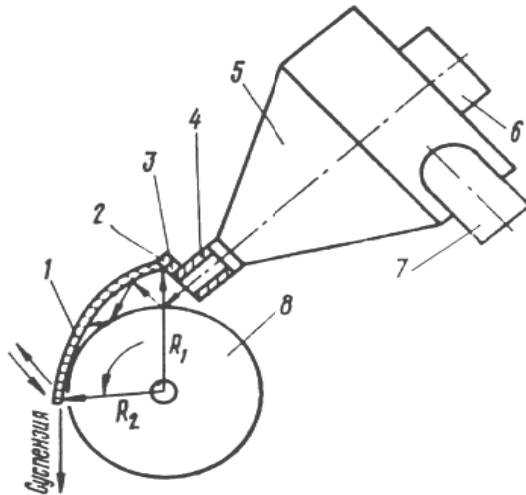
Струменевий апарат з екраном для обробки зовнішніх поверхонь труб: 1 – еластичний екран; 2 - вісь; 3 - кронштейн; 4 - сопло; 5 - корпус струминного апарата; 6 - штуцер подачі води; 7 - штуцер подачі абразиву; 8 - оброблювана труба
